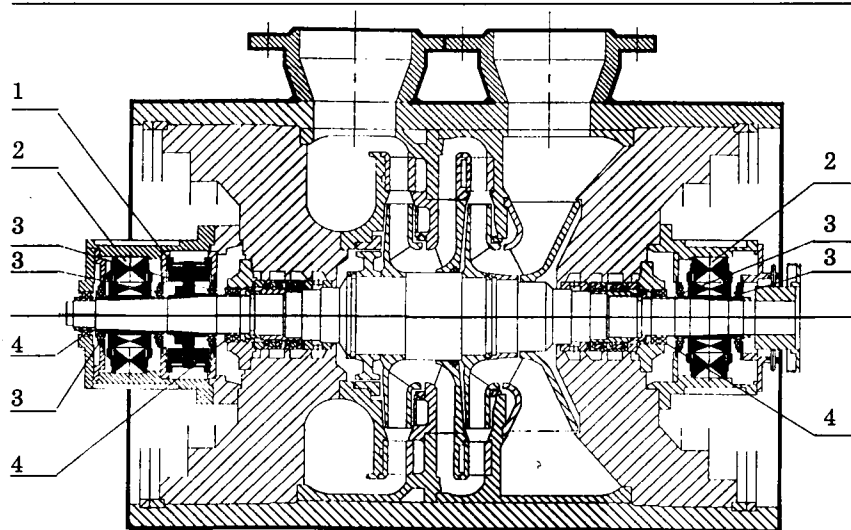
Конструкция компрессора с электромагнитными подшипниками: 1 — осевой подшипник; 2 — радиальный подшипник; 3 — датчик положения ротора; 4 — страховочный шарикоподшипник
